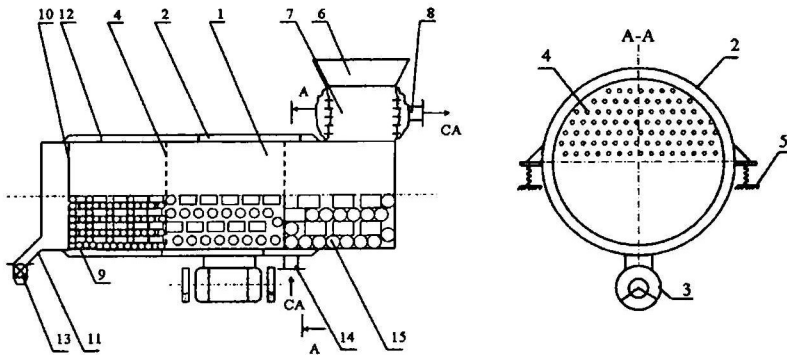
Вибрационная сушилка-мельница непрерывного действия. 1 – корпус; 2 – теплообменная рубашка; 3 – инерционный вибратор; 4 – перегородки секций; 5 – упругие опоры; 6 – загрузочный бункер; 7 – загрузочный рукав; 8 – патрубок отвода сушильного агента; 9 – мелющие тела; 10 – торцевая стенка корпуса; 11 – выгрузочный патрубок; 12 – штуцер подачи; 13 – затвор сушильного агента.
